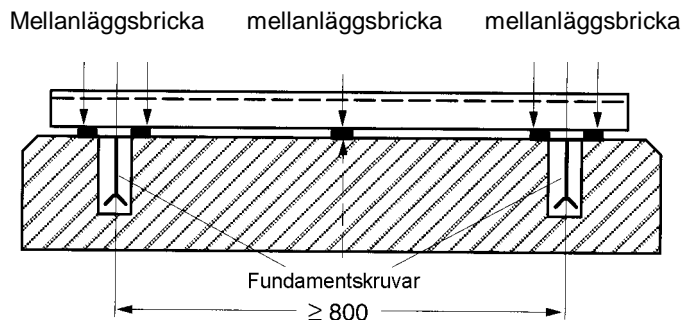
placering av erforderliga mellanläggsbrickor.
